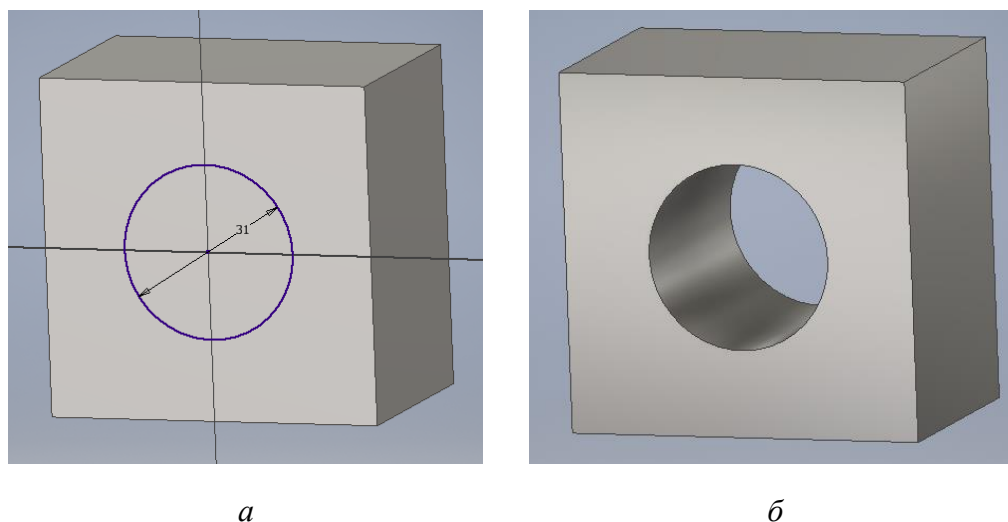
Эскиз окружности (а) и сквозное цилиндрическое отверстие (б) корпуса
